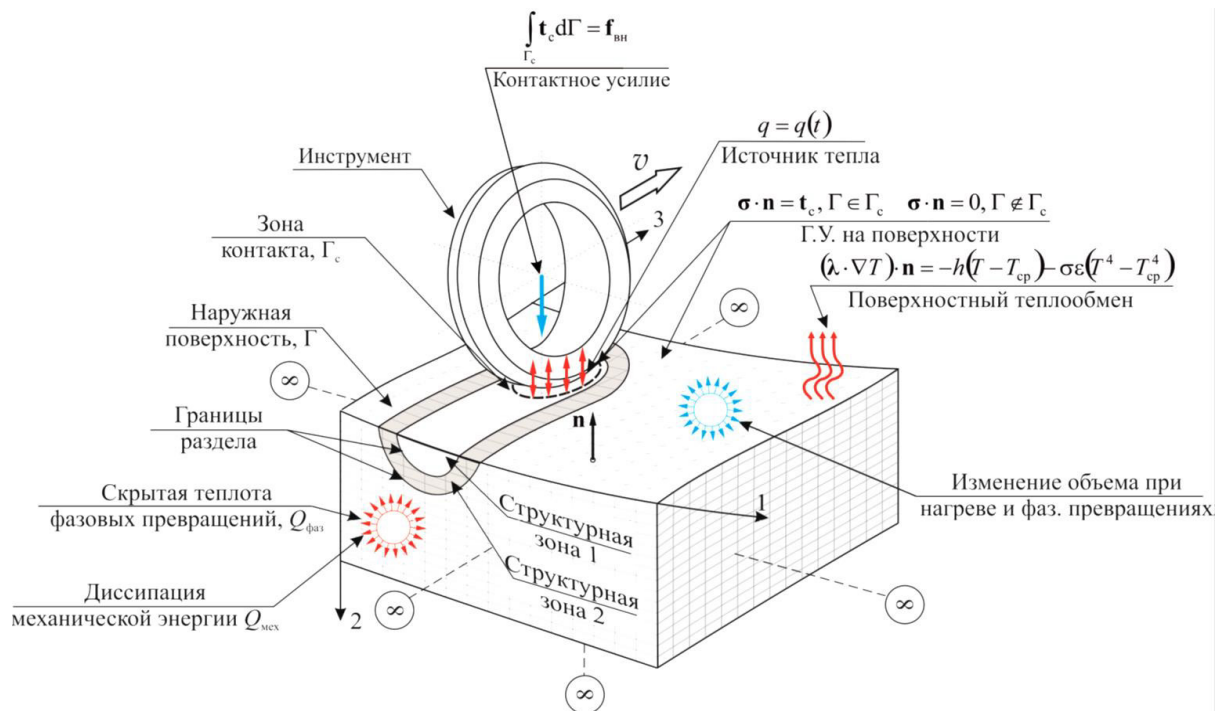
Электромеханическая обработка детали твердосплавного инструмента в форме ролика
